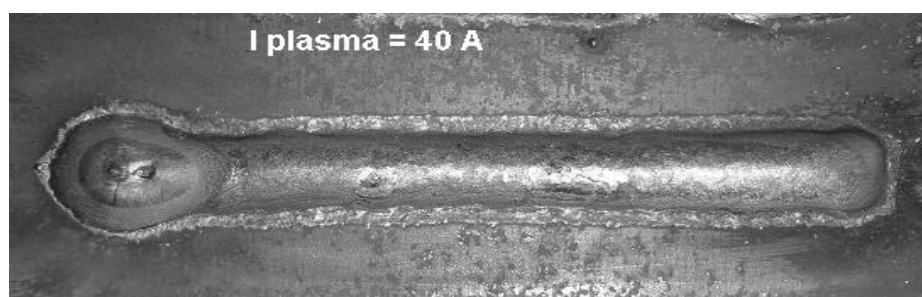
Cordão de solda realizado com os parâmetro do teste 3
